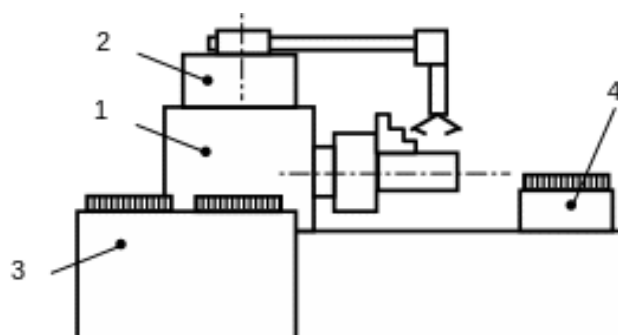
Схема ГПМ с промышленным роботом на шпиндельной части станка: 1 – станок мод. 1720Т1; 2 – промышленный робот; 3 – накопитель заготовок и деталей; 4 – инструментальный магазин
